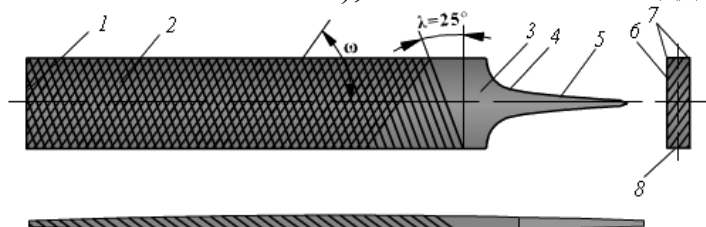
Слюсарний напилок загального призначення: 1 — носок; 2 — робоча частина; 3 — ненасічена ділянка; 4 — заплечико; 5 — хвостовик; 6, 8 — широка та вузька сторони; 7 — ребра
